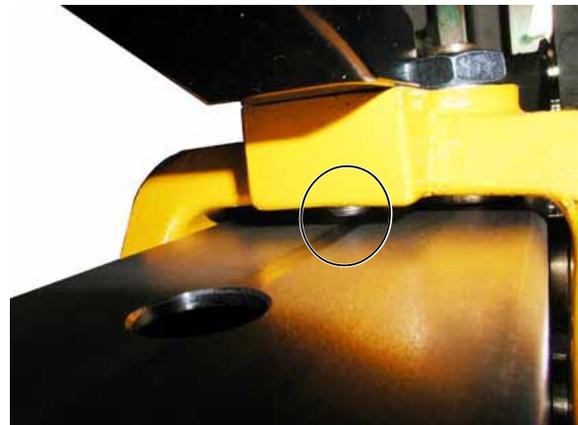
Notwendiges Spiel zwischen Führungsschlitten-Schrauben und Bohrsäule
